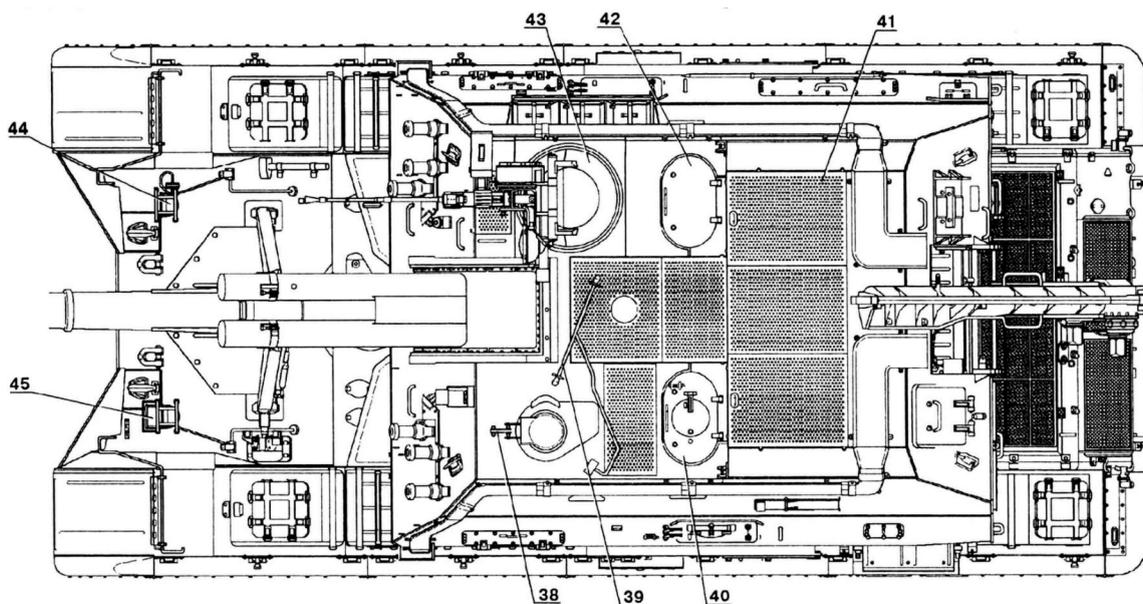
Чертеж СГ 2С19 (вид сверху)
